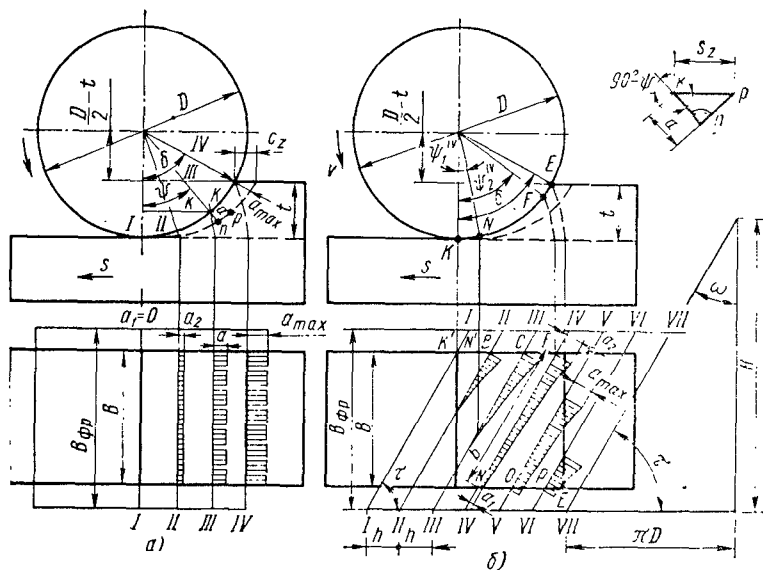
Элементы резания при работе цилиндрической фрезой: а — с прямыми зубьями; б — с винтовыми зубьями
